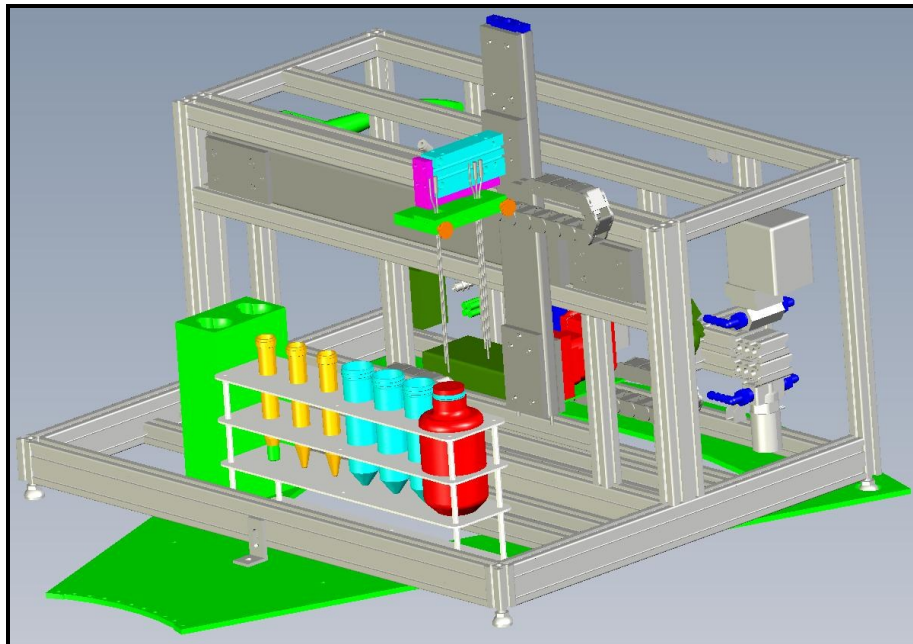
CAD-Model des Single Vessel -Liquid Handler
